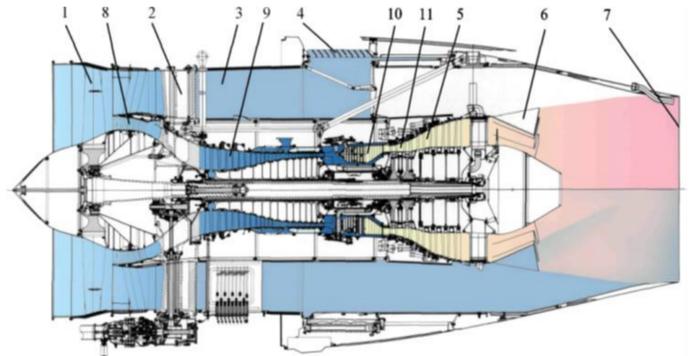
Схема ГТД. 1-вентилятор; 2-разделительный корпус; 3-канал наружного контура; 4-реверс тяги; 5-турбина вентилятора (низкого давления); 6-смеситель; 7-общее сопло; 8-подпорные ступени на валу вентилятора; 9-компрессор высокого давления; 10-камера сгорания; 11-турбина высокого давления
